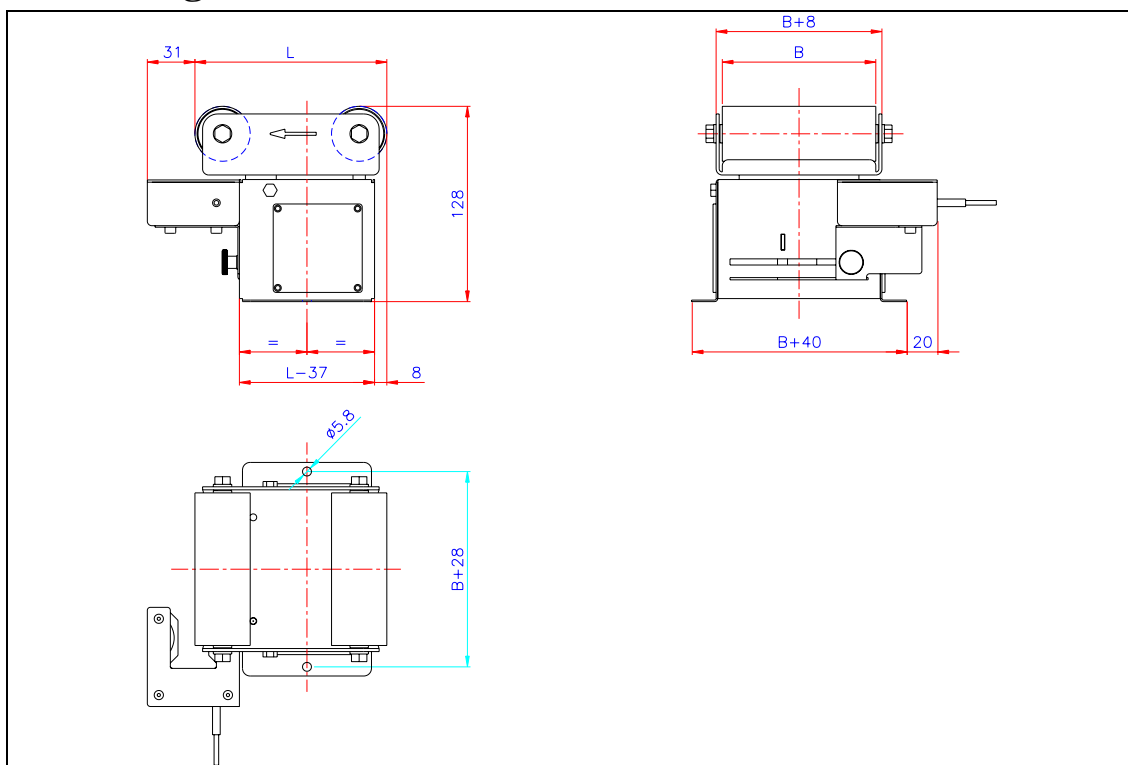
Prinzipskizze mit Dimensionen (BKS010)
